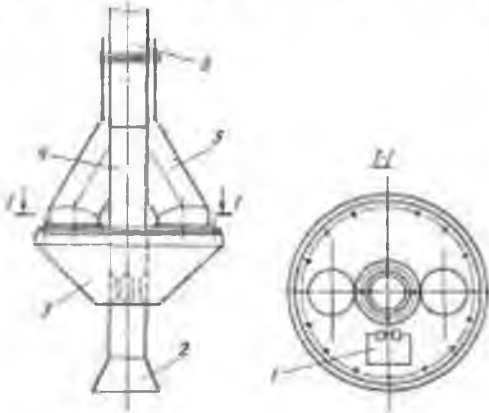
Приймач типу ПТО: 1-люк; 2-конфузор; 3-приймальна коробка; 4-труба; 5-самогечна труба; 6-зернопровід
